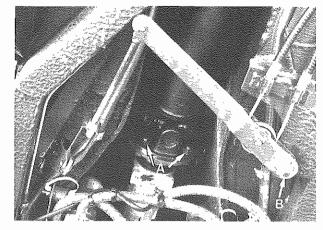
A - Viti fissaggio albero al cambio Screw fixing shaft to transmission B - Dado fissaggio leva freno a mano Hand trake lever nut
